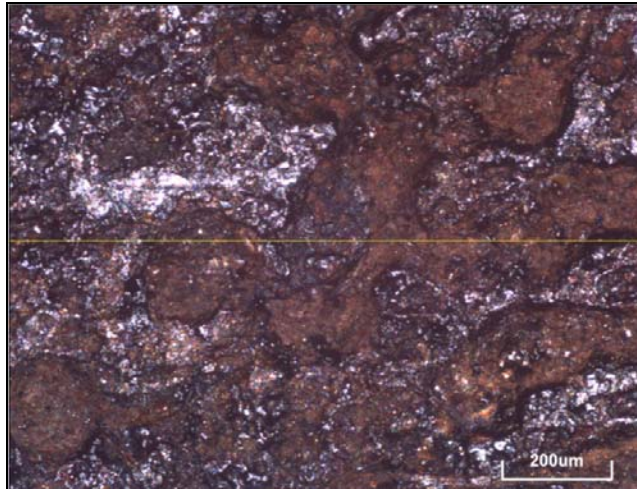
Superficie de la soldadura después del ensayo de SSC.
